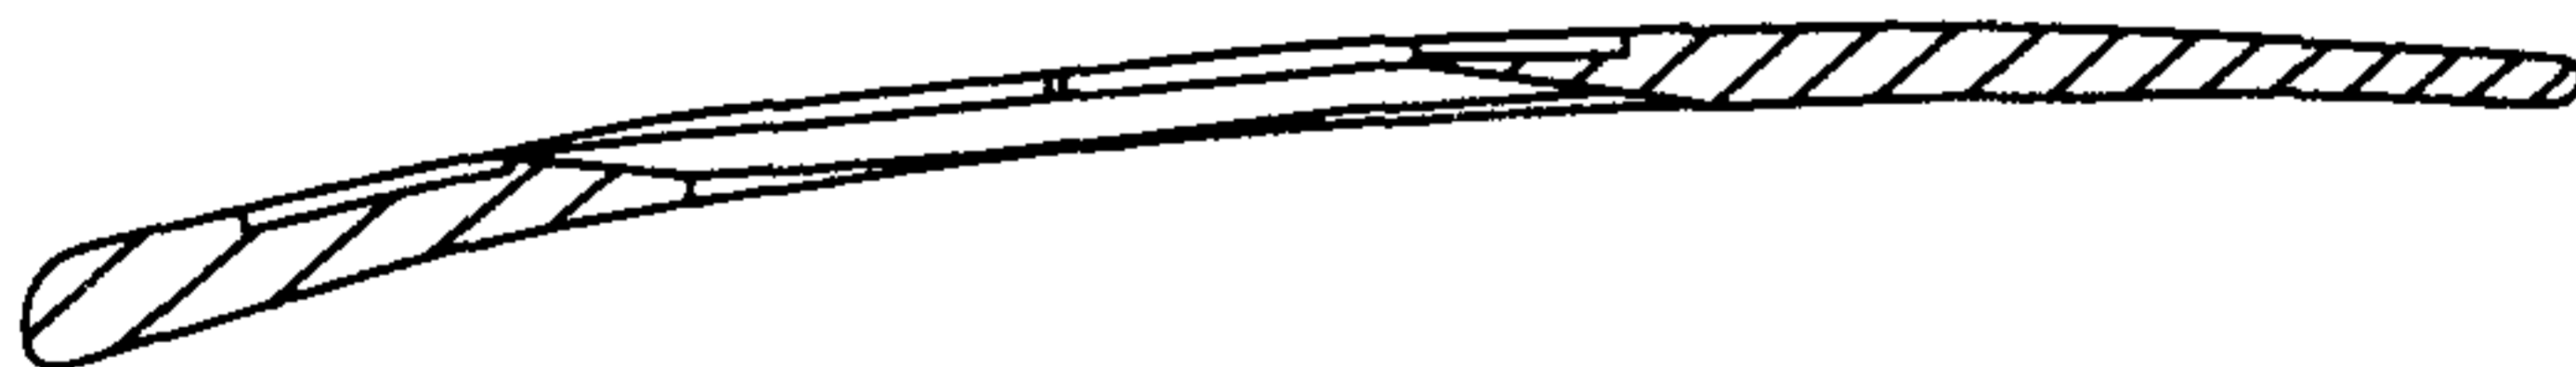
Контрольный образец № 1 с рисками, выходящими на кромку лопатки
